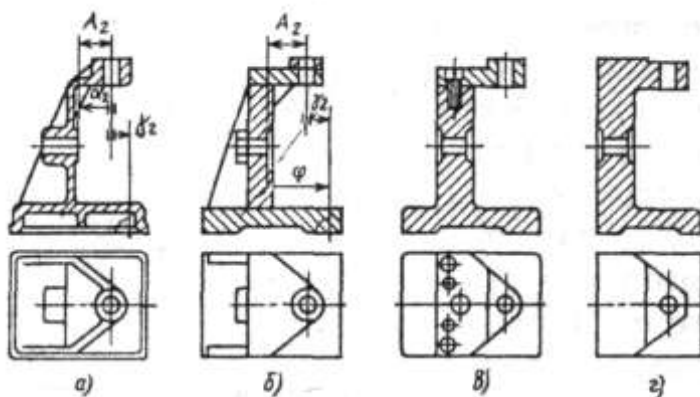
Влияние конструкции корпуса приспособления на его точность
